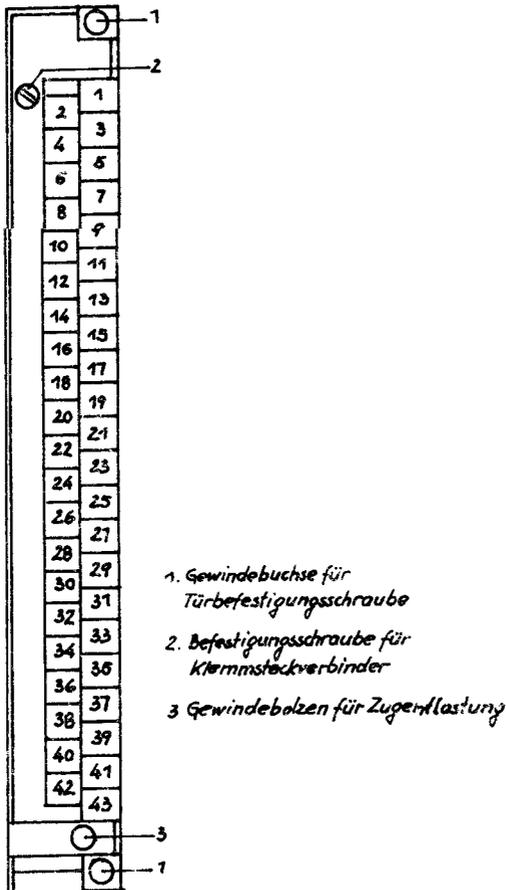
Klemmsteckverbinder mit Klemmennummerierung
